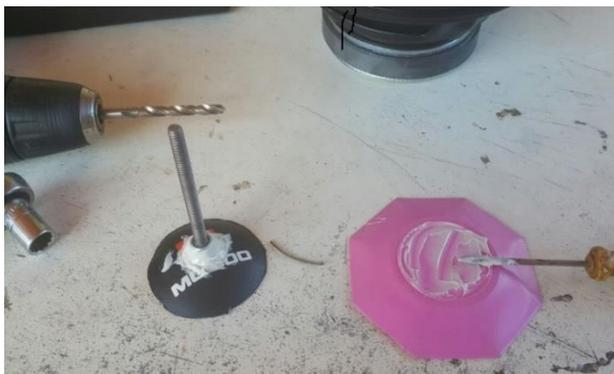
Eixo central para fixação da placa (Arquivo pessoal)
